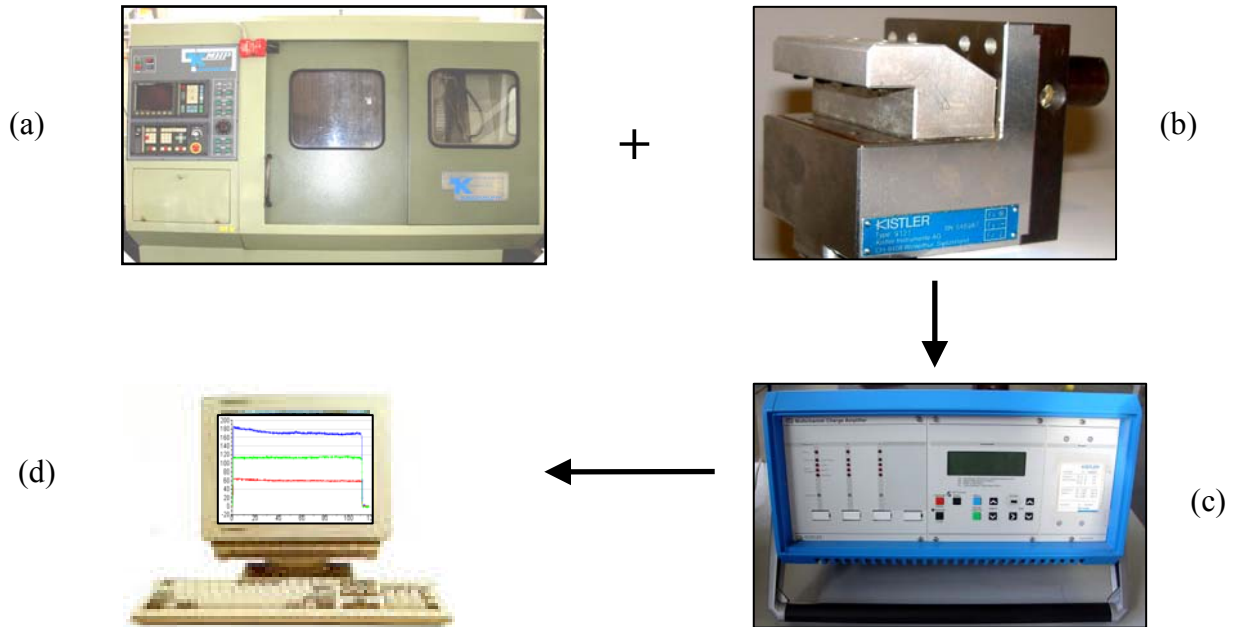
Equipamiento utilizado en la medición de las fuerzas de corte:
